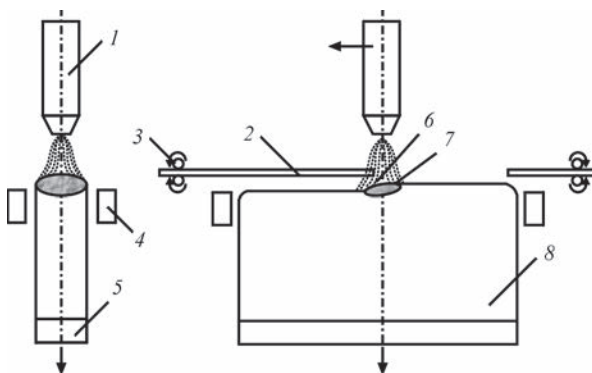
Схема установки для адитивного вирощування монокристалів тугоплавких металів із застосуванням плазмово-індукційного способу: 1 – плазмотрон; 2 – витратний пруток; 3 – механізм подачі прутків; 4 – індуктор; 5 – зародковий кристал; 6 – плазмова дуга; 7 – локальна ванна; 8 – монокристал
